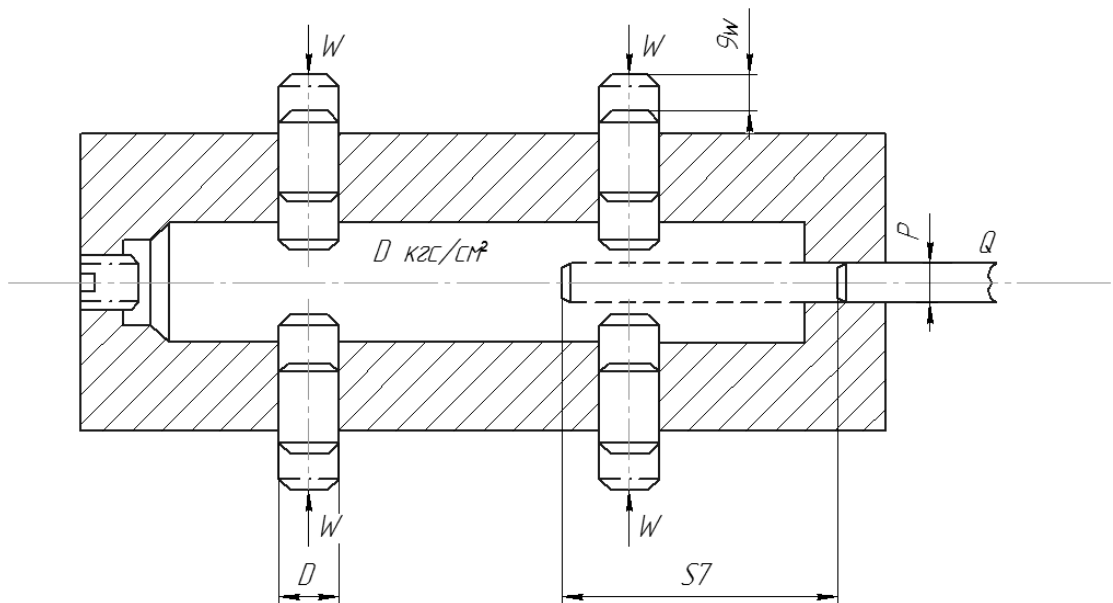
Схема для розрахунку багатоплунжерного механізму з
